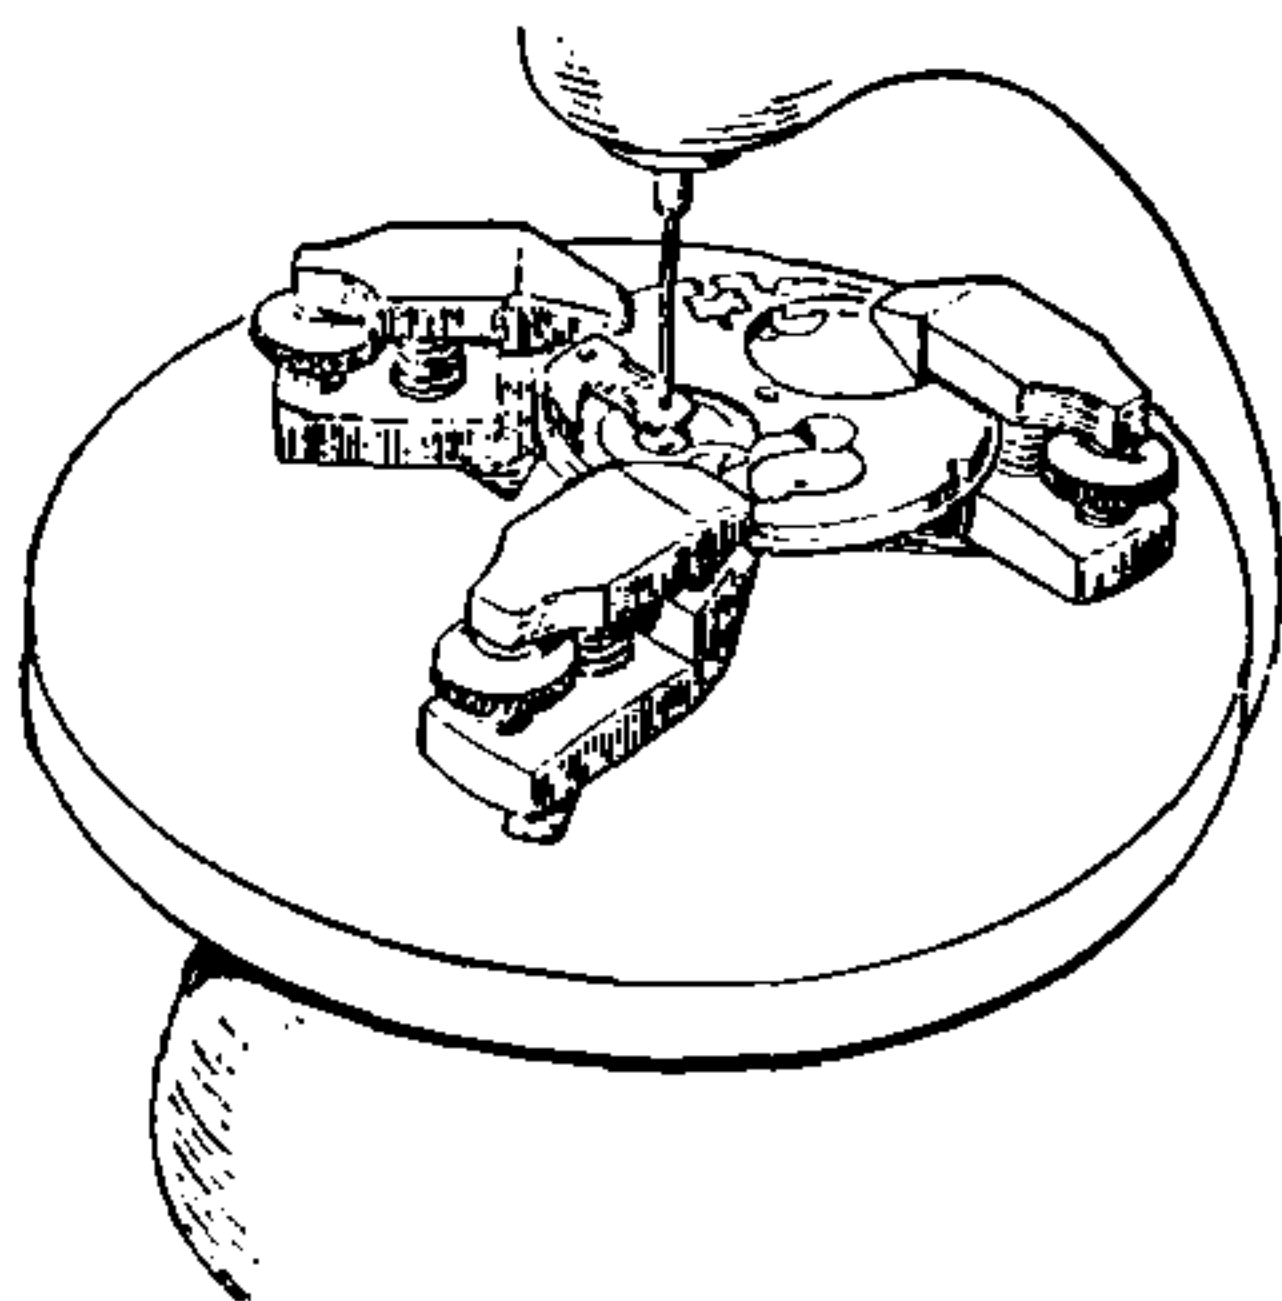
Dispositivo di fissaggio con cani per tenere in piano la platina.
